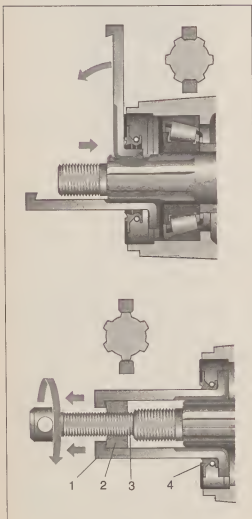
Выпрессовка сальника хвостовика редуктора: 1 – лапка (2 шт.); 2 – резьбовая втулка; 3 – винт; 4 – сальник
